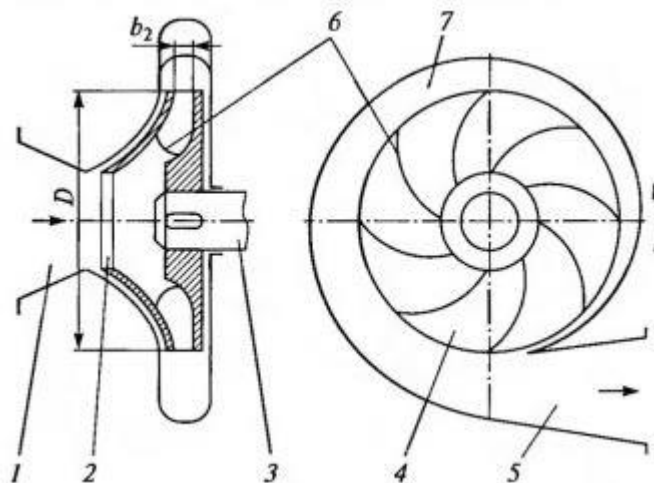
Схема центробежного насоса: 1 - всасывающий патрубок; 2 - входное отверстие рабочего колеса; 3 - вал; 4 - рабочее колесо; 5 - напорный патрубок; 6 - лопатка; 7 - спиральный отвод.
